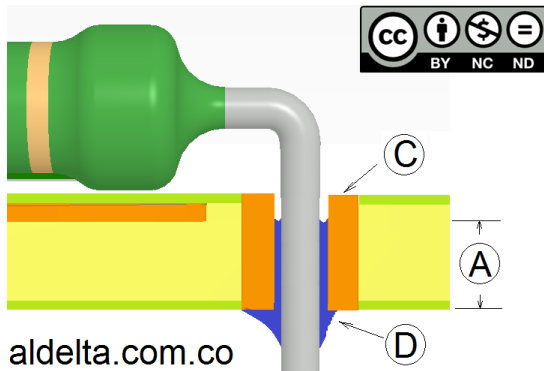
Criterios de aceptación de soldadura para componentes de inserción, THT según la IPC 610. Vista de perfil. Autoría propia.
